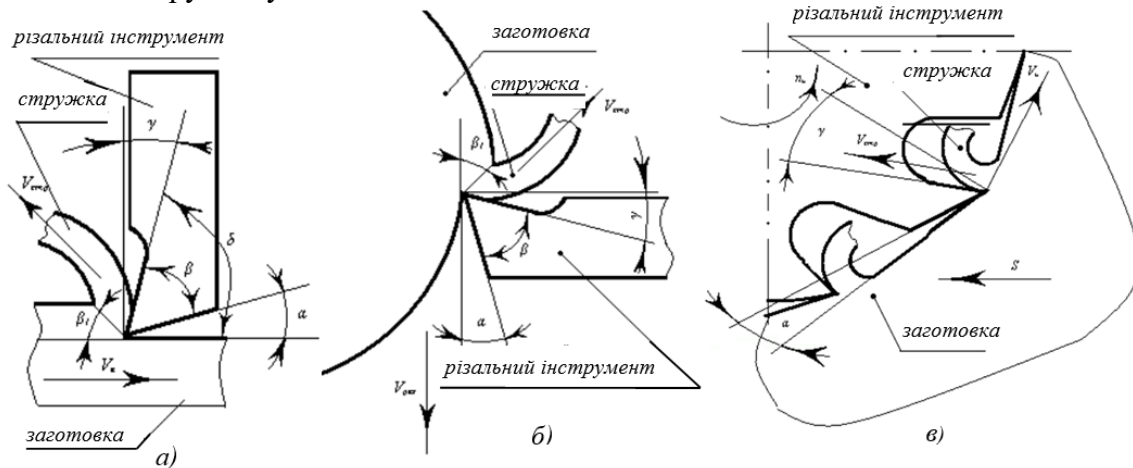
Традиційні схеми різання в процесах механічного оброблення:
